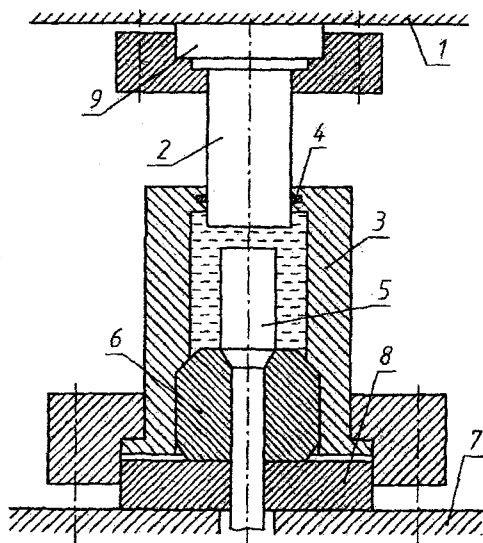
Схема одной из конструкций гидростата: 1 – ползун пресса; 2 – пуанжер; 3 – контейнер; 4 – уплотнение пуанжера в контейнере; 5 – заготовка; 6 – матрица (коническая посадка); 7 – стол пресса; 8 – прокладка закаленная; 9 – прокладка закаленная (для снижения контактного давления в 15...20 раз)
